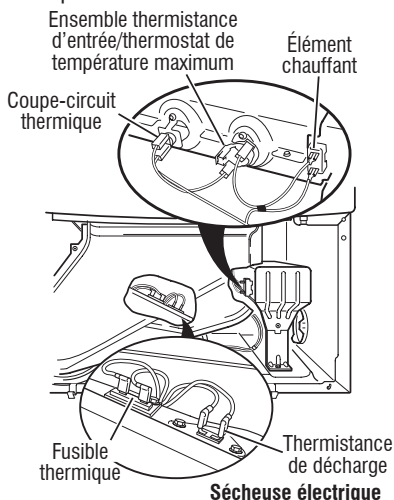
Composants thermiques, sècheuse électrique, vue de face.
